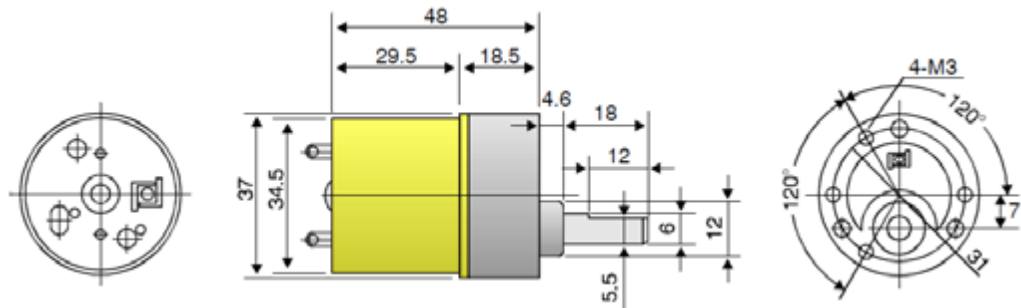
A. Motor D.C. con caja reductora SAYAMA-Gearhead Motor ³⁰⁶
